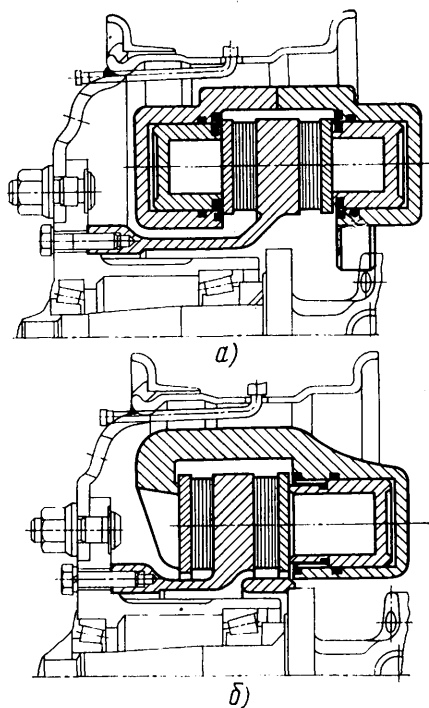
Компонка дискового тормоза с фиксированной (а) и плавающей (б) скобой в ободу переднего колеса грузового автомобиля
